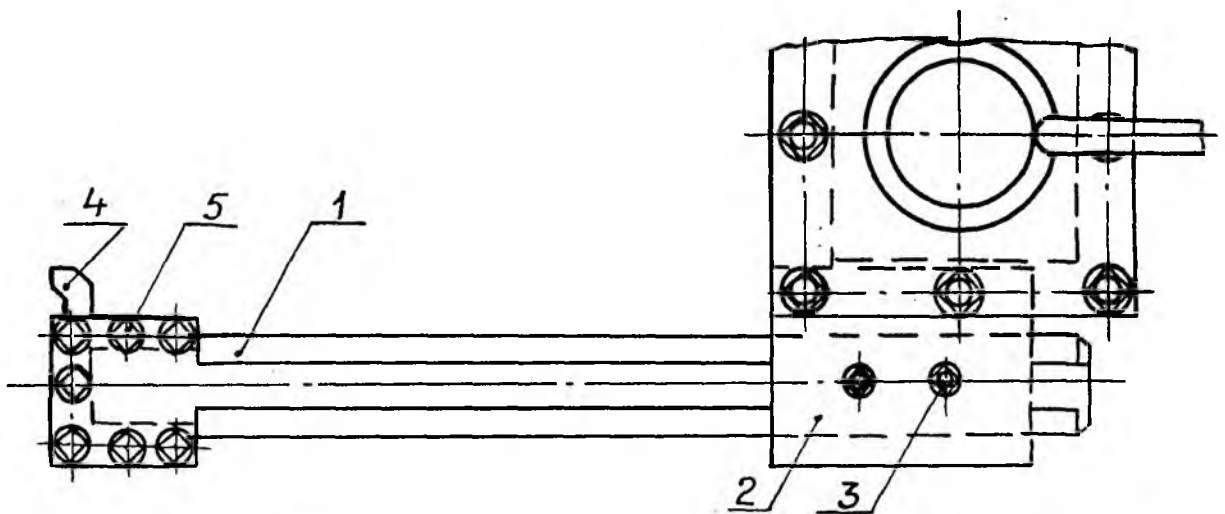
Резцовая оправка для обработки деталей над выемкой в станке.
